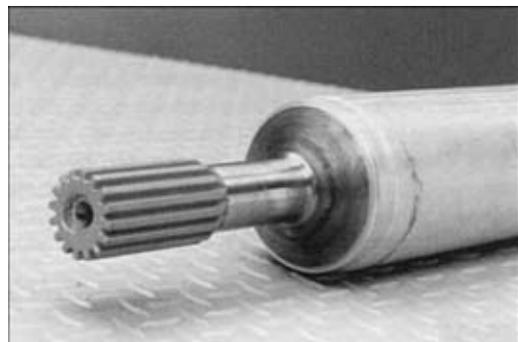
Сталеалюминиевый вал, сваренный способом МИС
